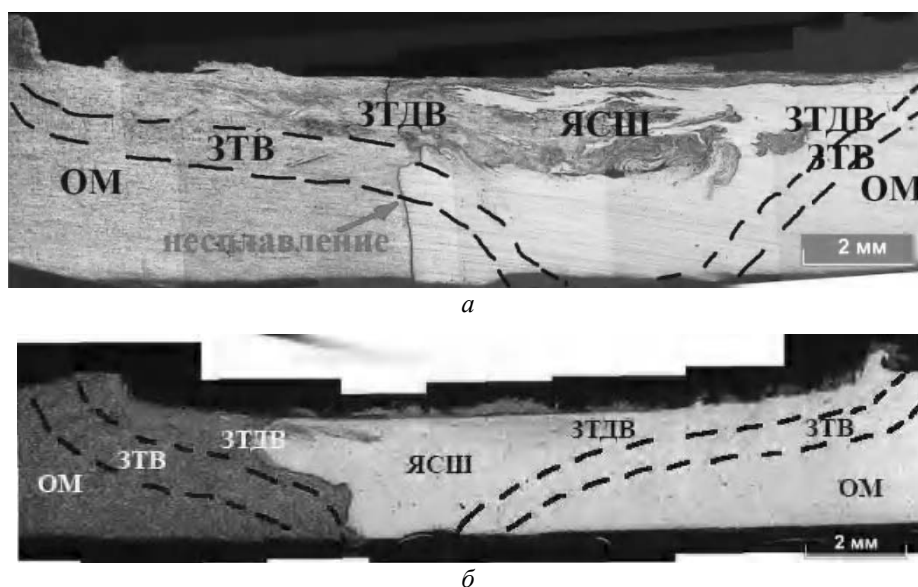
Макрошлиф сварного шва алюминия и меди:
